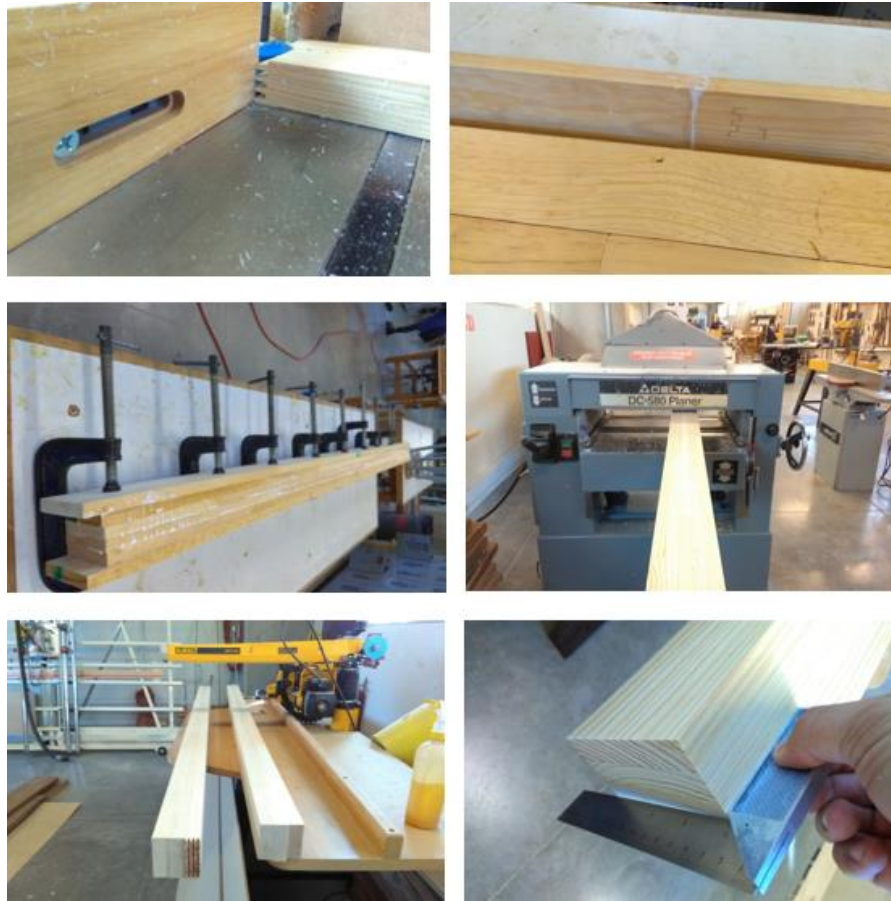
Fabricación de columnas y vigas de madera laminada (Elaboración propia).
